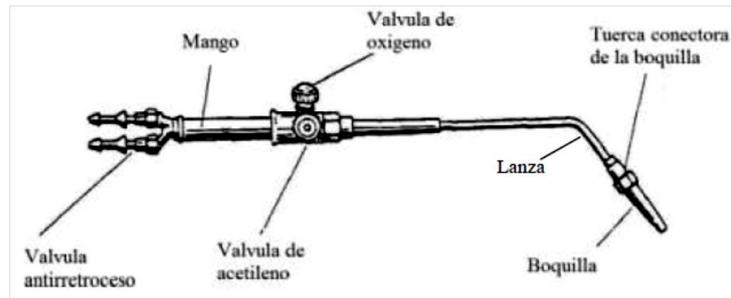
Elementos de que consta un equipo de soldadura oxiacetilénica.
